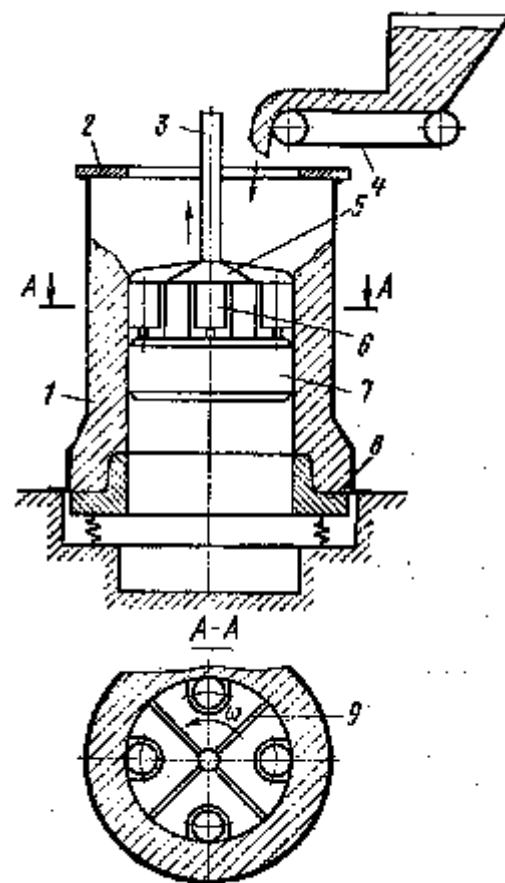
Схема установки для радиального прессования железобетонных труб
